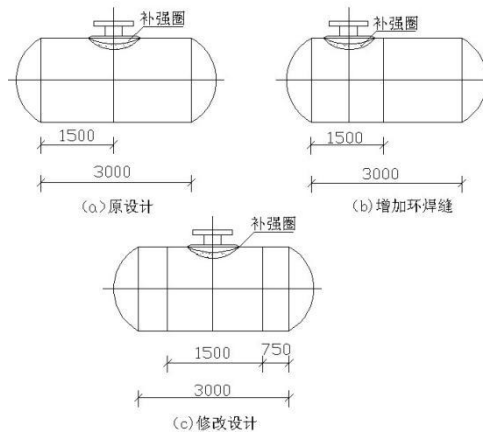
焊缝覆盖对焊缝排布的影响示意图
